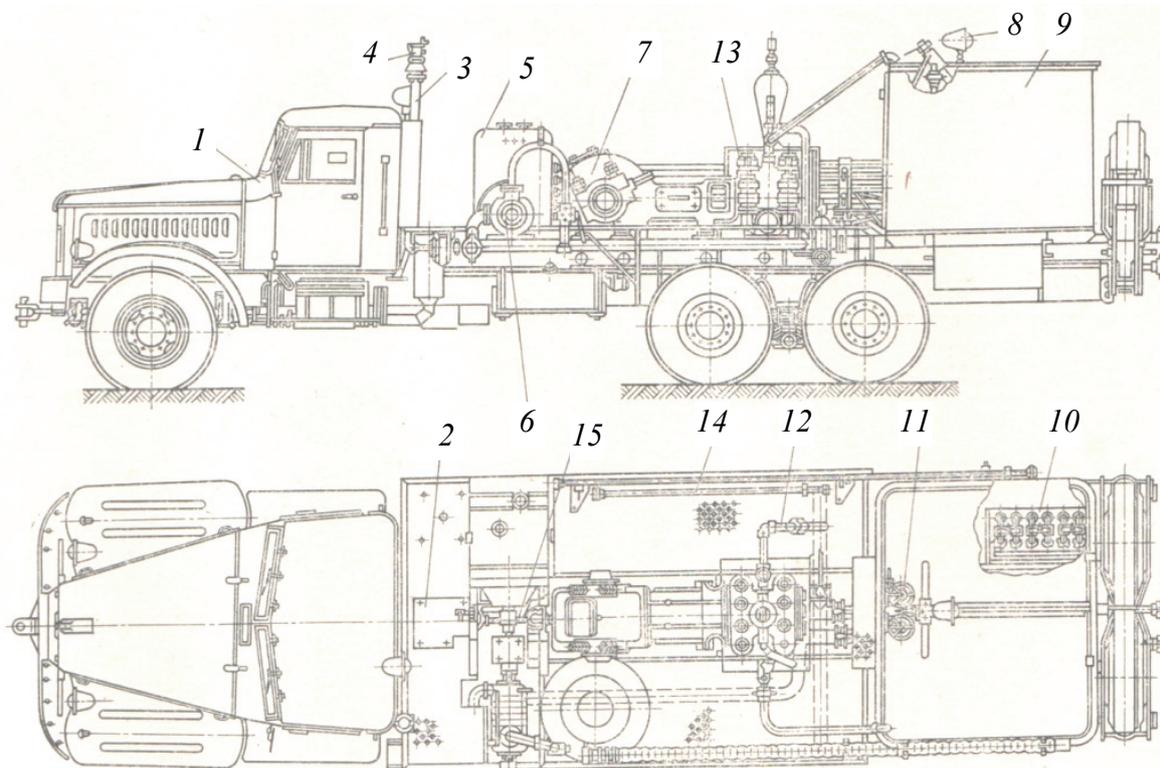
Цементировочный агрегат ЦА-А 320А: 1 – шасси автомобиля; 2 – коробка отбора мощности; 3 – выхлопная труба; 4 – искрогаситель; 5 – двигатель ГАЗ-51А; 6 – центробежный водоподающий насос; 7 –цементировочный насос 9Т; 8 – фара; 9 – мерный бак; 10 – колено гибкого металлического шланга; 11 – донные клапаны; 12 – нагнетательный трубопровод; 13 – кожух ограждения насоса; 14 – труба гибкого металлического шланга; 15 – карданный вал
